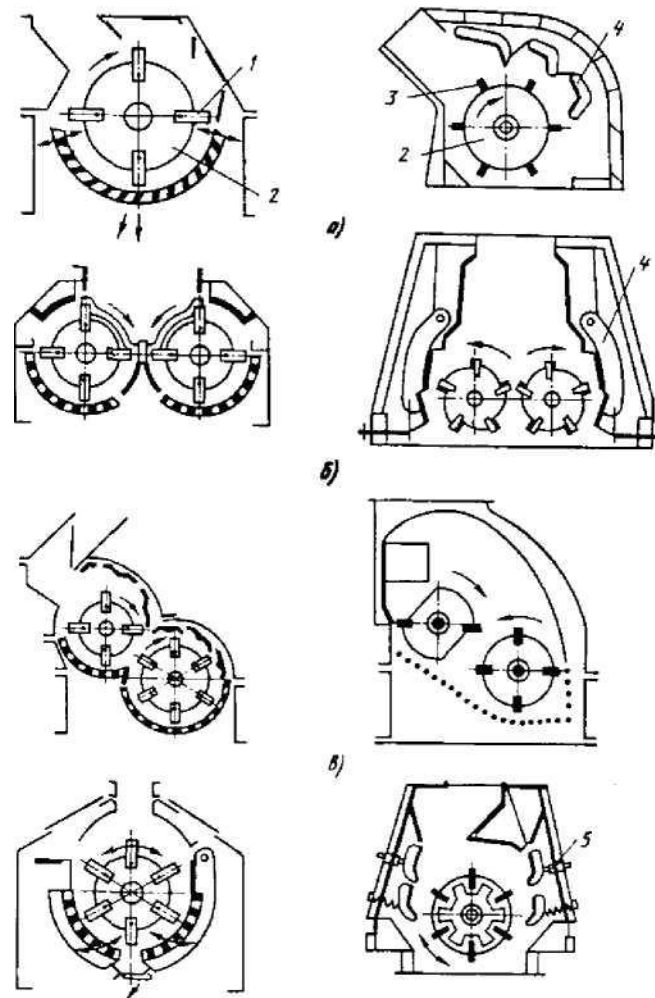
Основные схемы молотковых и роторных дробилок: а - однороторные; б - двухроторные одноступенчатого дробления; в - двухроторные двухступенчатые; г - реверсивные; 1 - молоток; 2 - ротор; 3 - била; 4 - отражательные плиты; 5 - механизм регулировки зазора между билами и плитами
